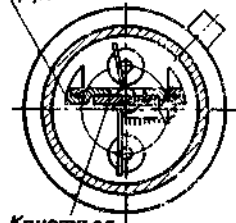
Конструкция корпуса КТ-21. Вариант для монтажа кристалла на керамический держатель.
